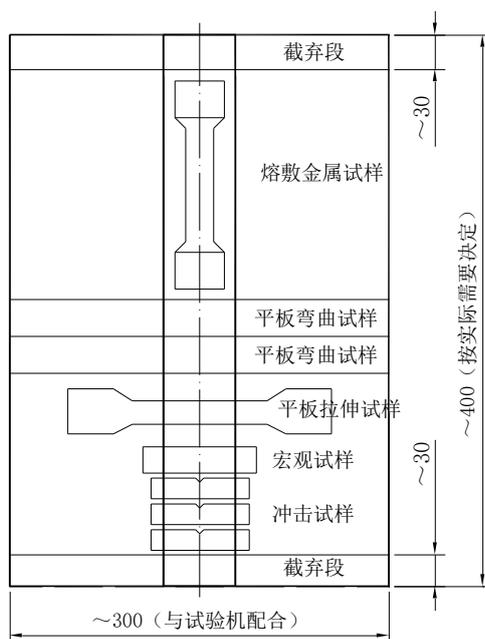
锅炉及压力容器对接焊试件的取样位置
